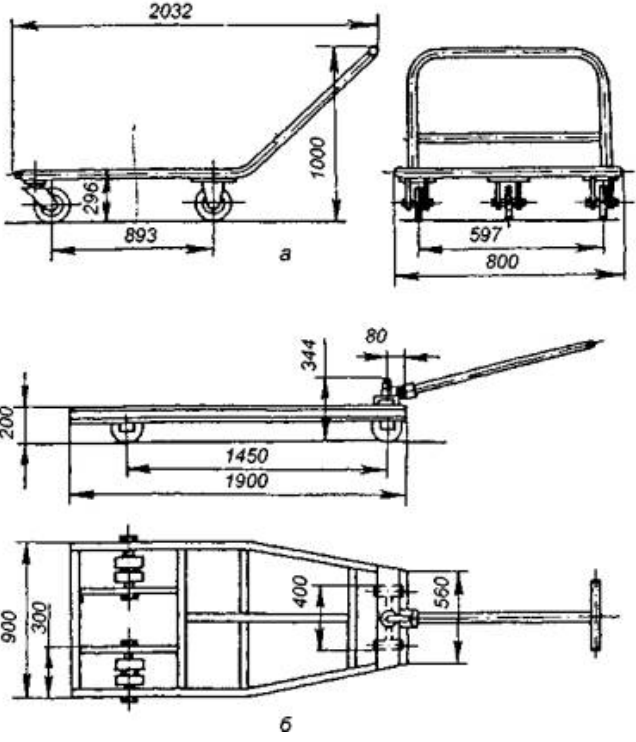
Тележки для перевозки грузов и монтажных заготовок:
